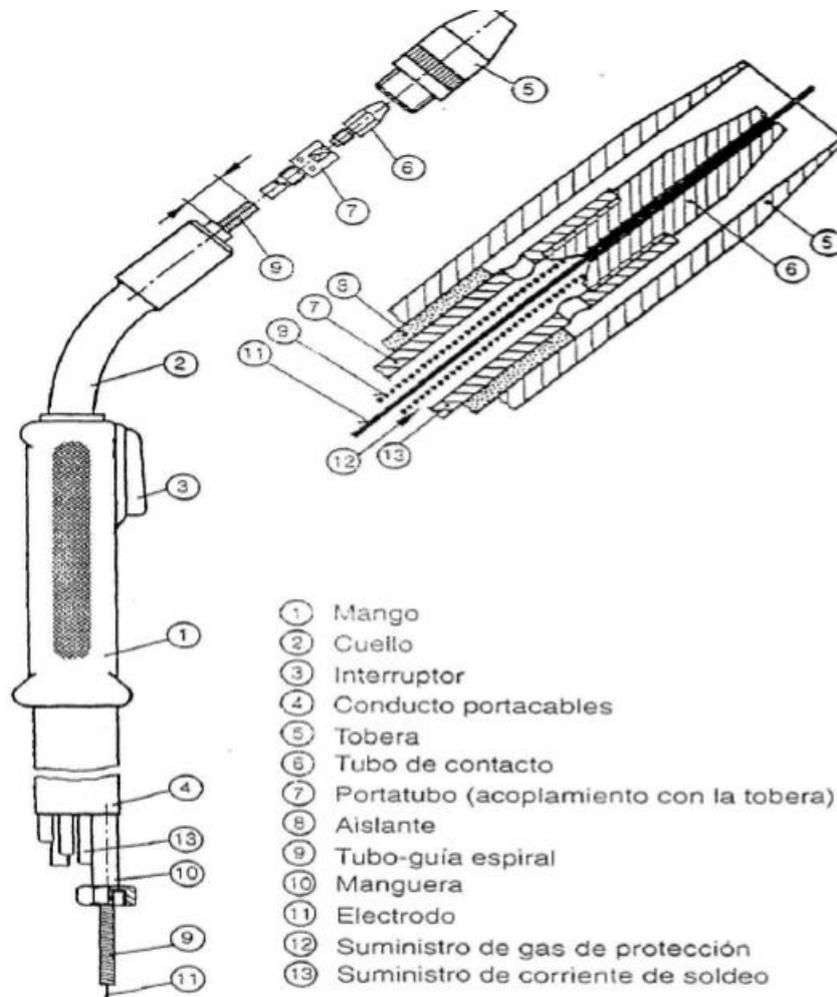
Pistola para soldeo MIG/MAG (acero al carbono)
